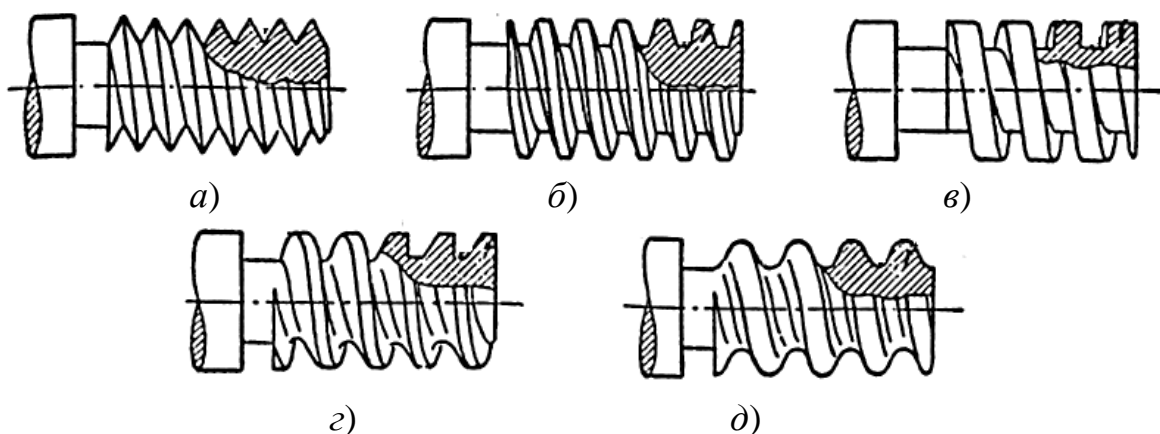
Профили резьбы: а – треугольный; б – трапецидальный; в – квадратный; г – упорная резьба; д – трубная резьба
